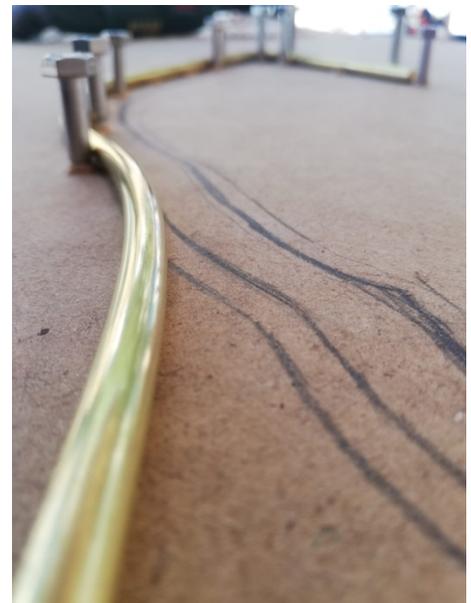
Proceso de construcción. Moldeado del latón, 2020.
